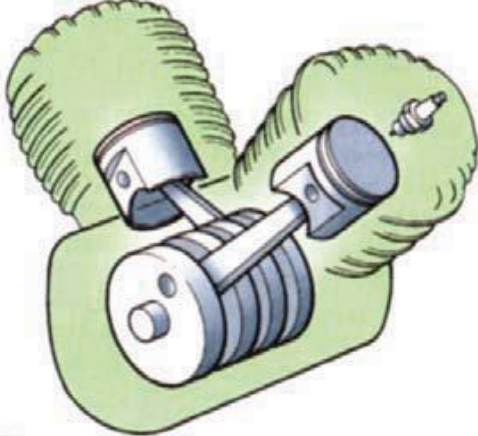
langkah bersilinder 2 kembar 360<sup>0</sup>
